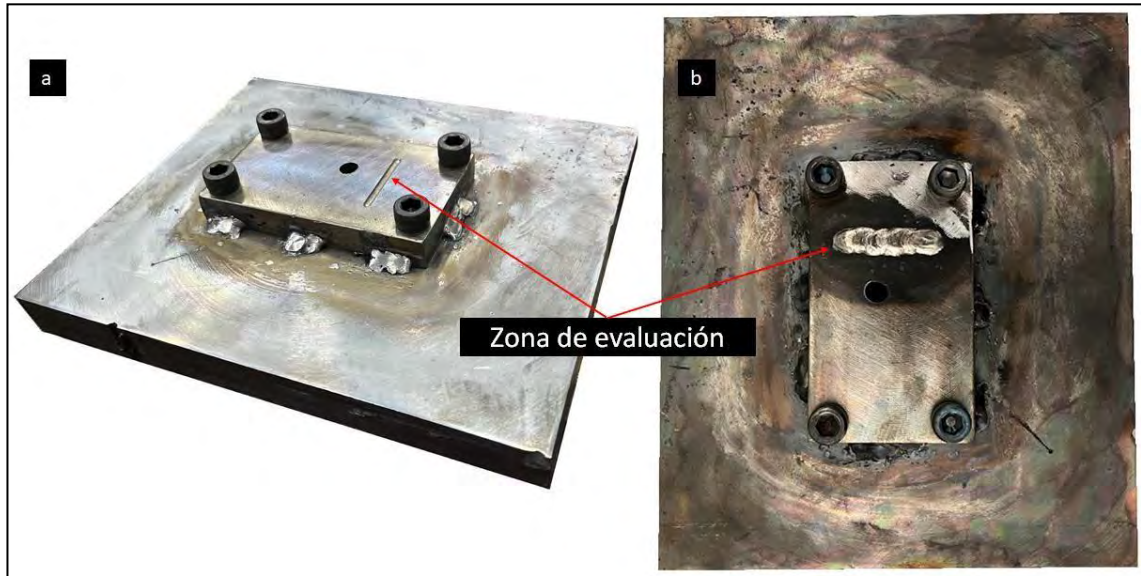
Montaje de ensayo EE del monoblock, (a) antes del cordón de soldadura en la zona de evaluación, (b) luego del cordón de soldadura en la zona de evaluación.
